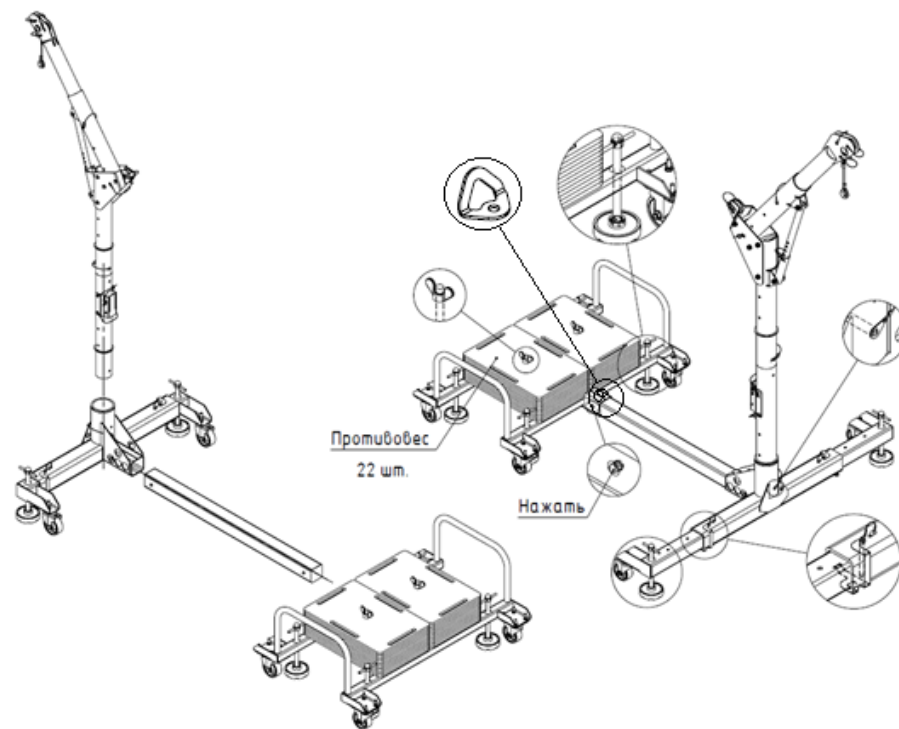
Монтаж СОБ Кран Е11-4Н
